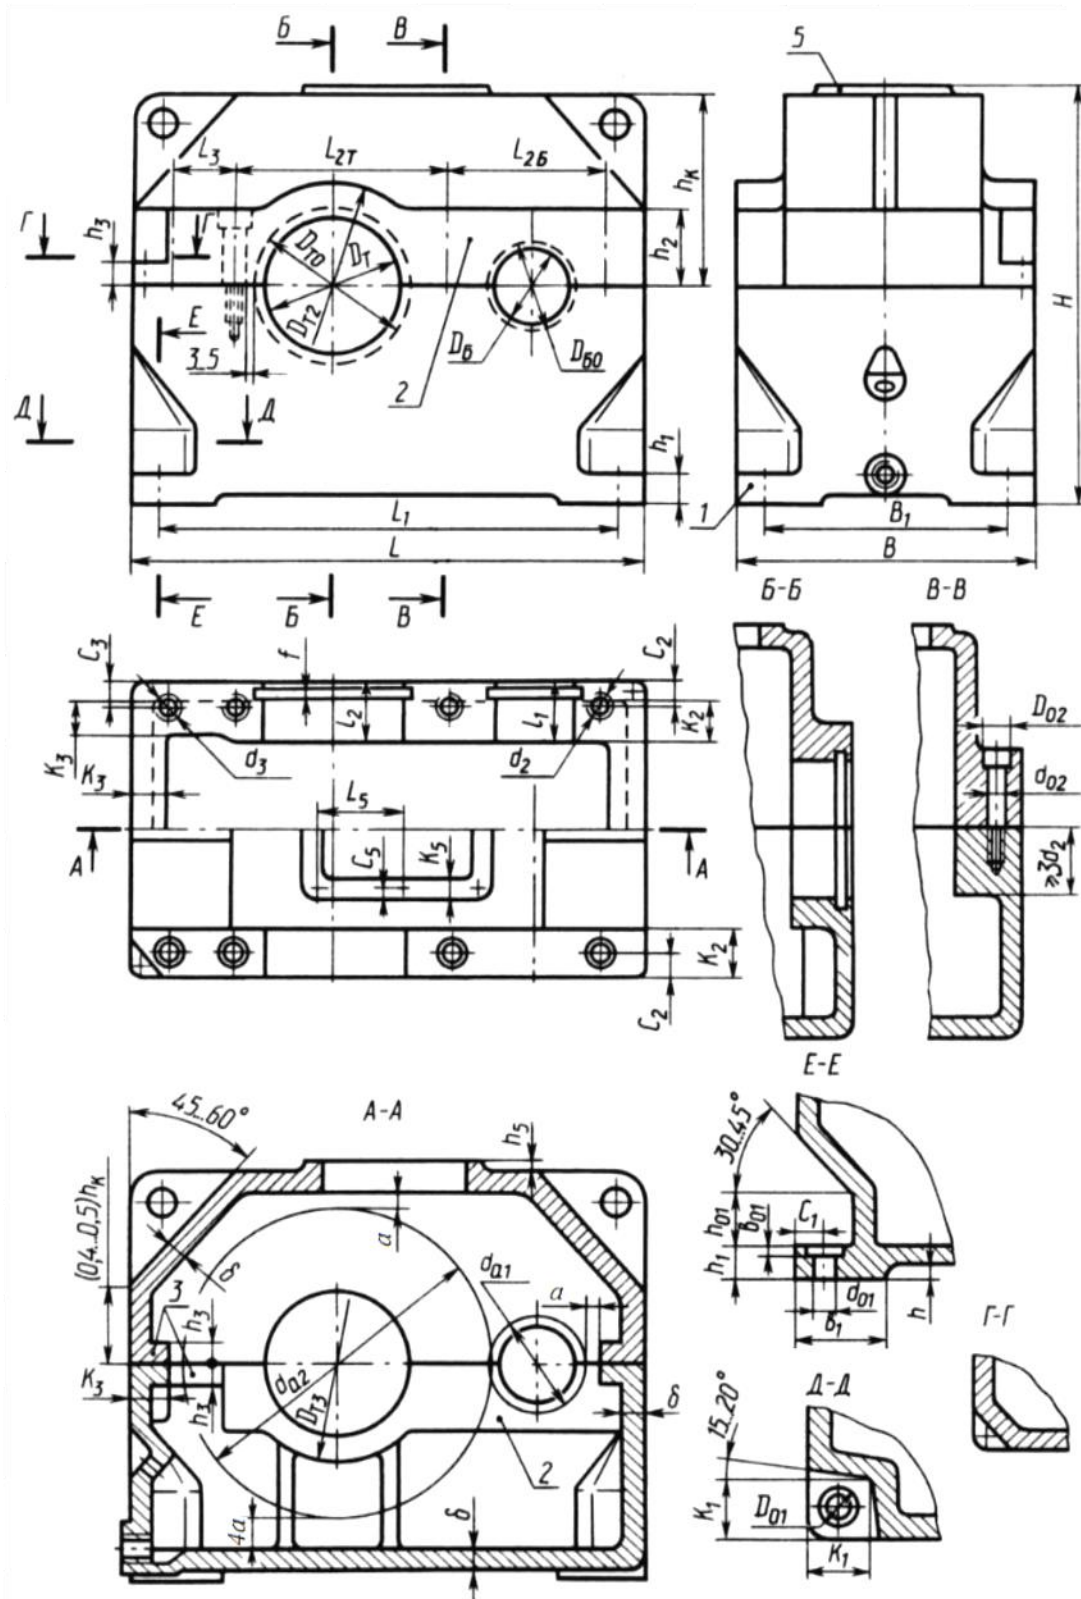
Разборный корпус одноступенчатого горизонтального редуктора
